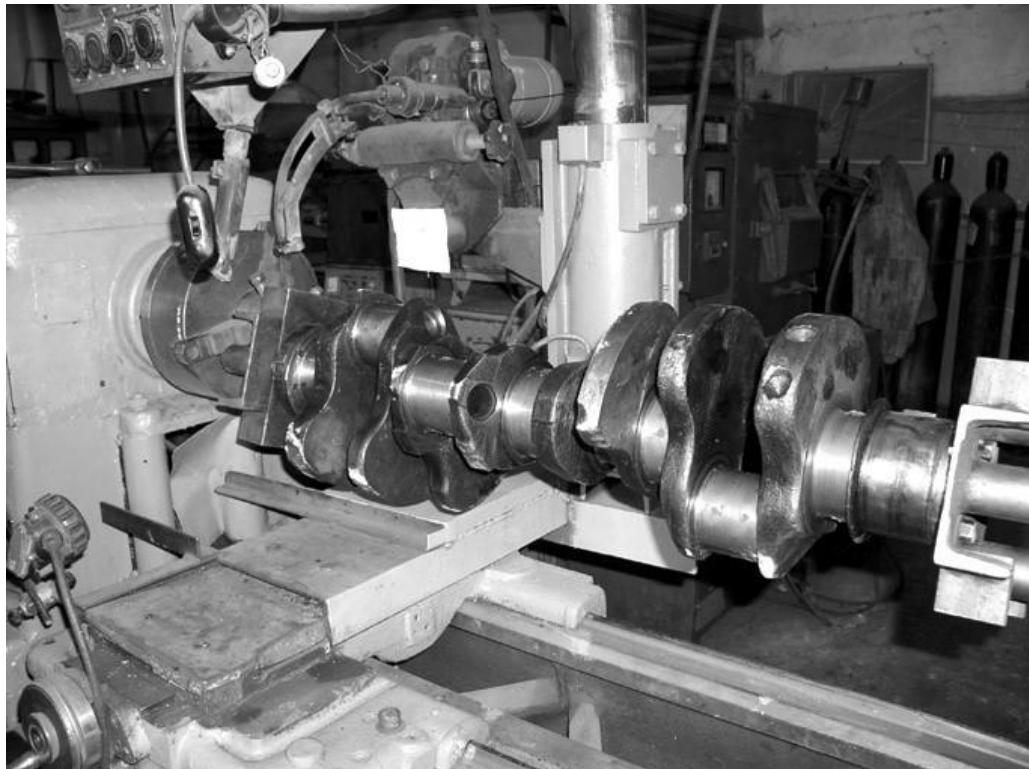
б. Переустаткований токарно-гвинторізний верстат моделі 1К62 з наплавочною головкою А-580М і джерелом живлення дуги ВДУ-506 (вид із центрозміщувач й наплавлюваним колінчатим валом)
